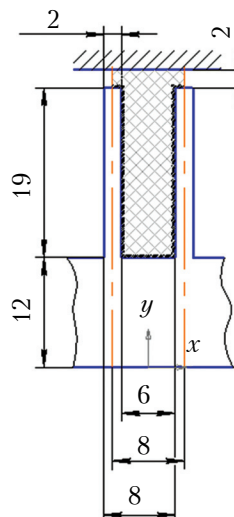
Місцевий поперечний розріз несучої основи з ребрами
